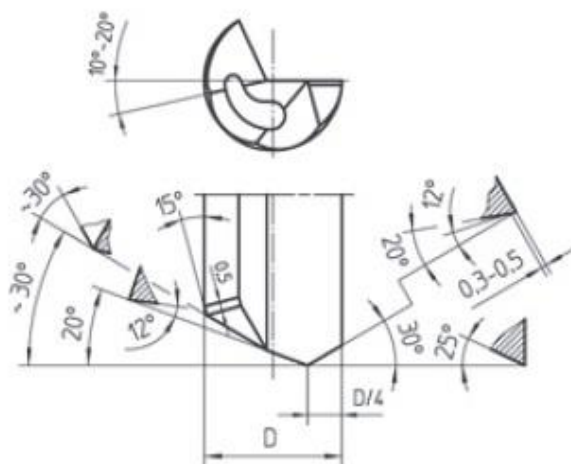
Стандартная заточка для диапазона сверления 4,001 – 20,000 мм
